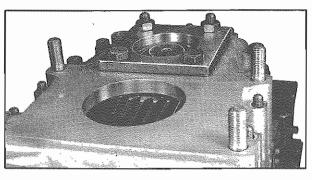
Controllo della posizione dell'albero secondario Checking the bearing of countershaft
